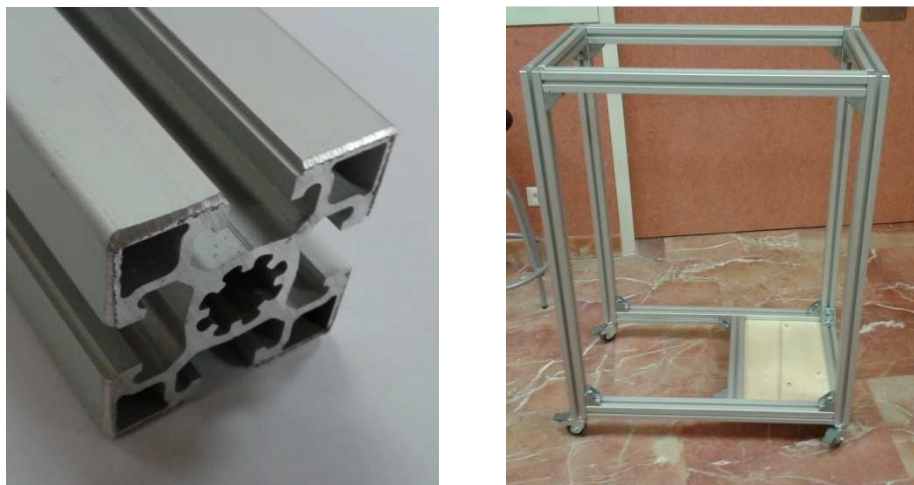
Perfil de aluminio utilizado e imagen de la estructura básica
